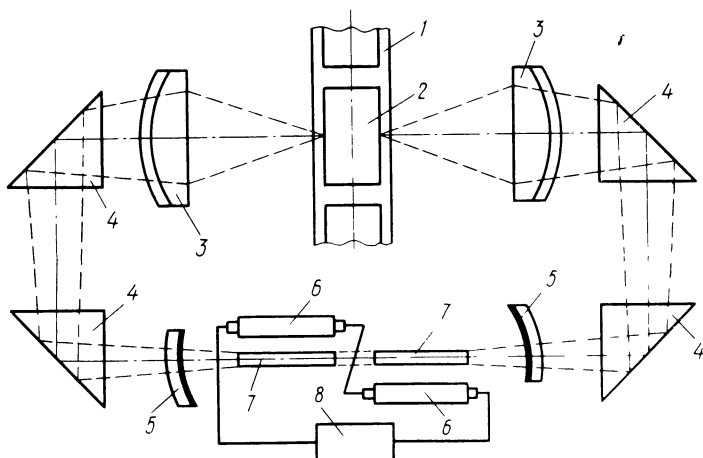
Схема полуавтоматической двухлучевой лазерной установки для герметизации корпусов микросхем:
